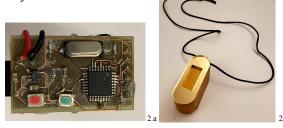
a visar PCB-kretsen. Bild 2.b visar smycket.
